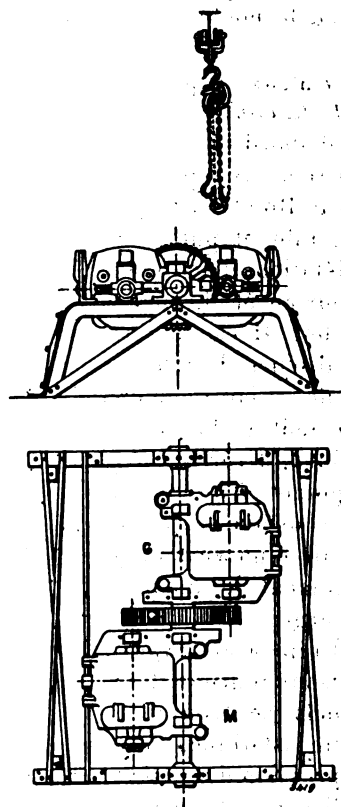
Élévation et vue en plan du châssis pour essais de moteurs de tramways.
